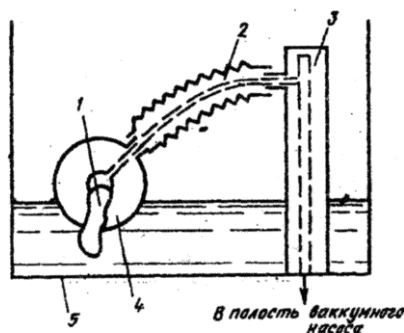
Регулювання витрати оливи: 1 – гніт; 2 – гнучкий елемент; 3 – корпус; 4 – поплавець; 5 – бачок
